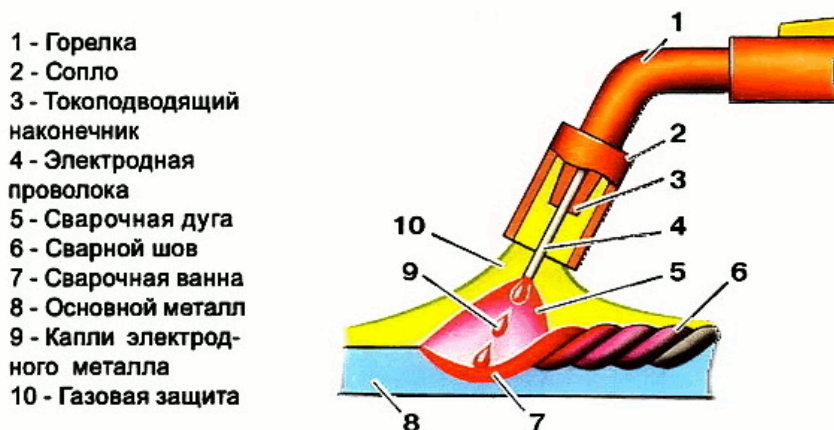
Схема сварки в среде углекислого газа
